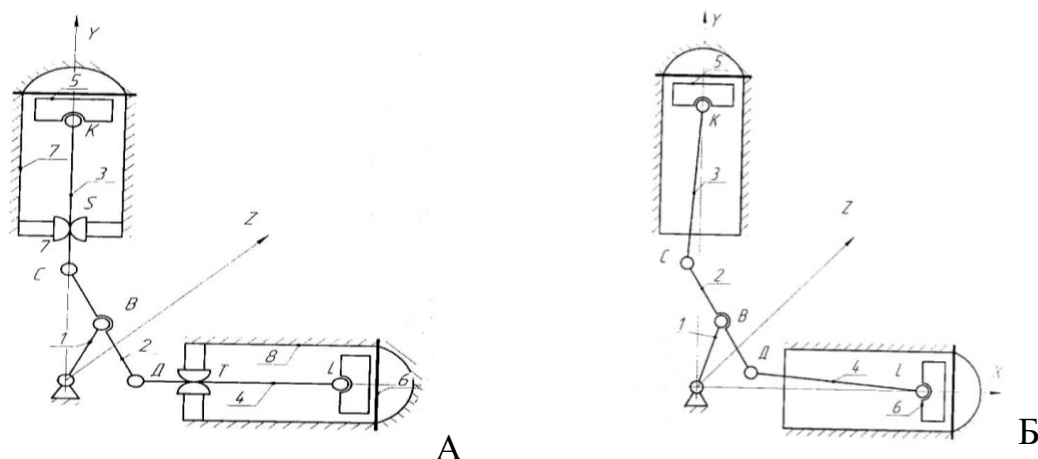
Кинематическая схема установки упора шатуну: А – с упором, Б – без упора
